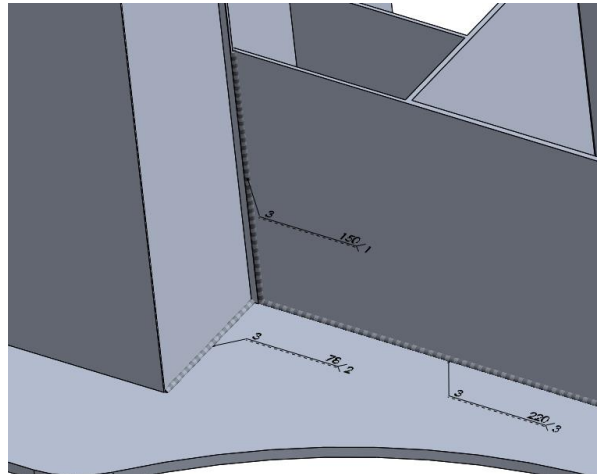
Cordones de soldadura 1, 2 y 3.
